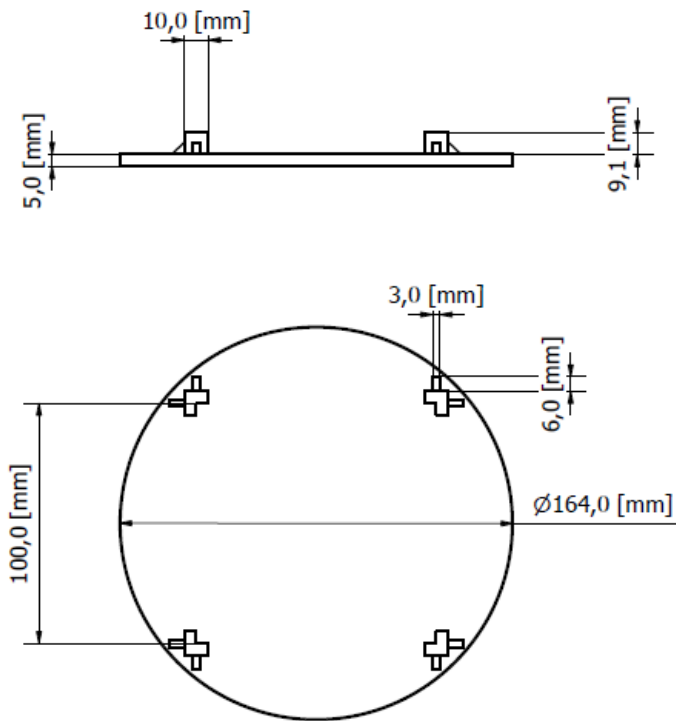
Base para apoyar el CubeSat en el banco de pruebas plano
